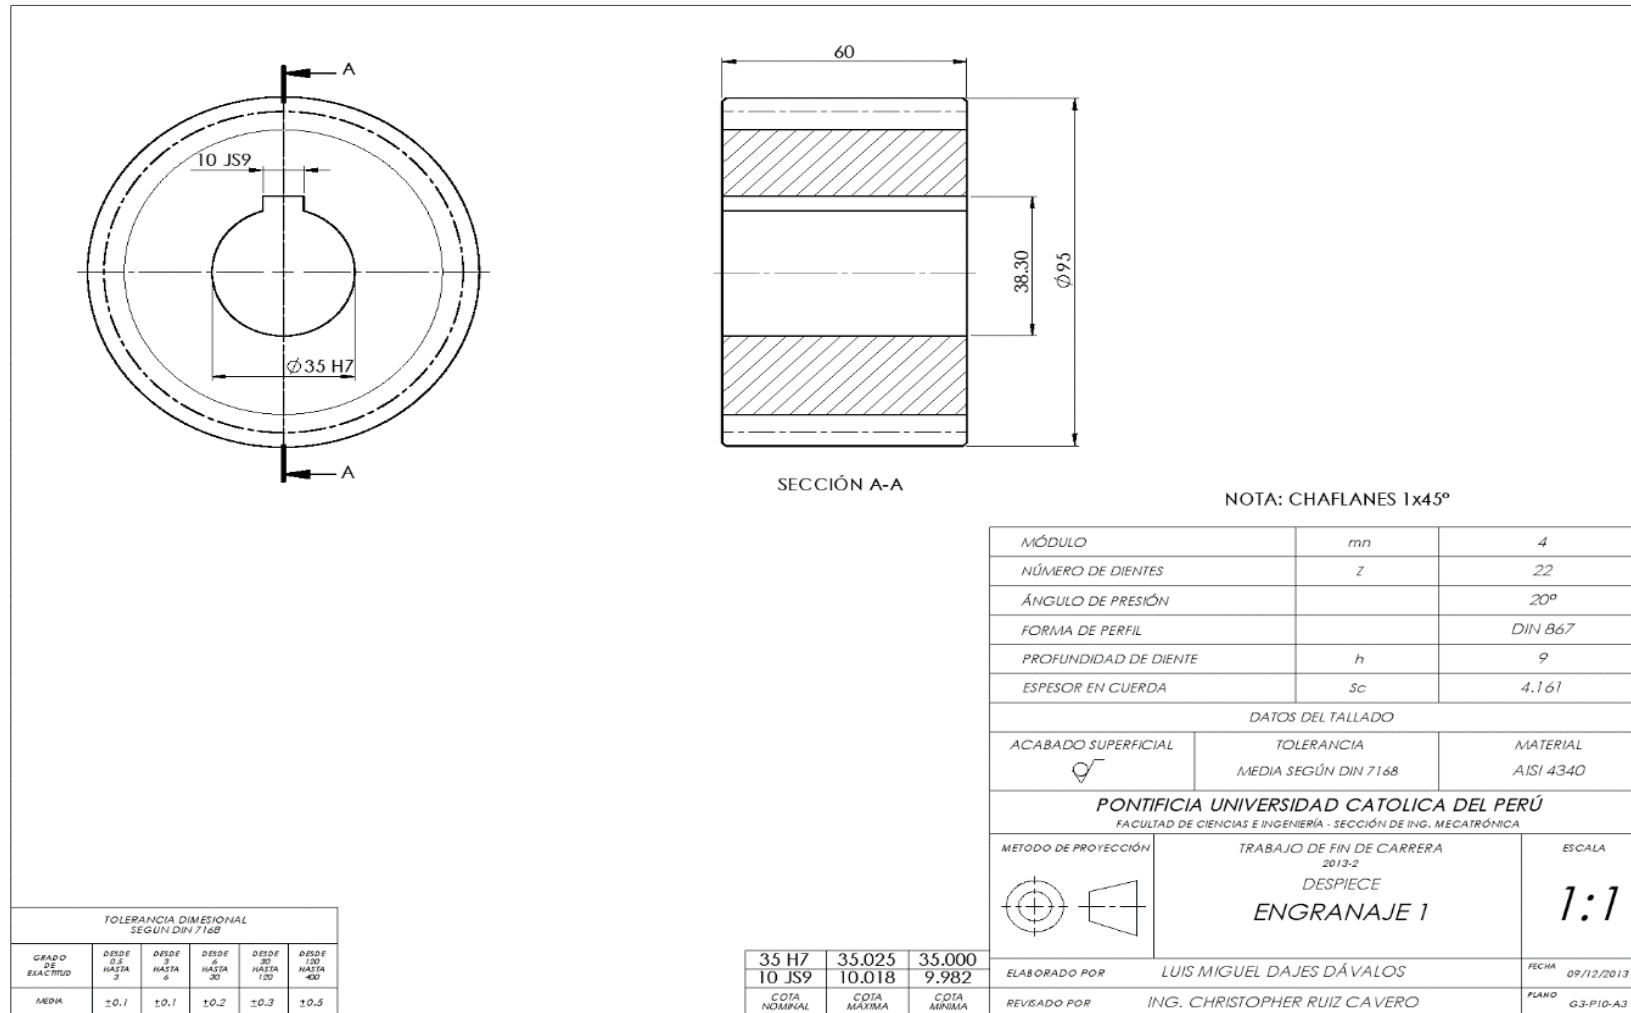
Plano de despiece del engranaje 1. Fuente: Elaboración propia.
